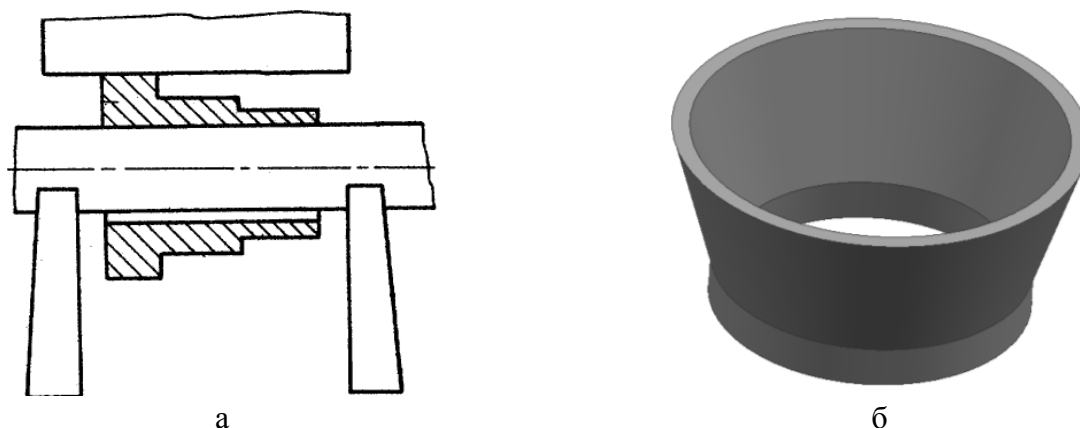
Пример использования ступенчатой заготовки (а) для получения конусной поковки (б)
